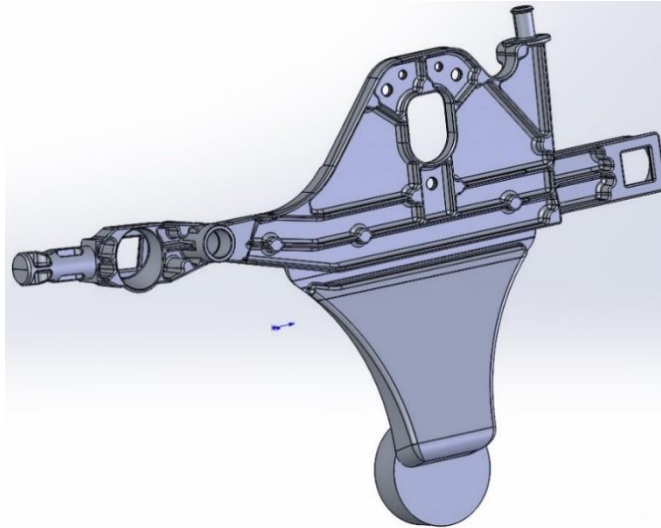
Отливка «Корпус» с литниковой системой
